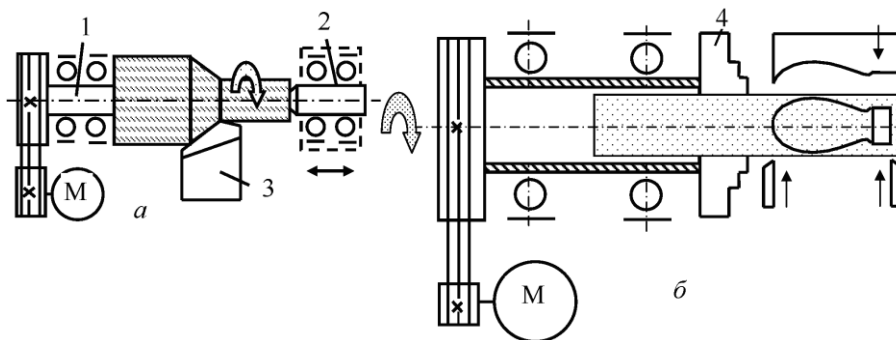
Обробка деталей: а - у центрах; б - у патроні
